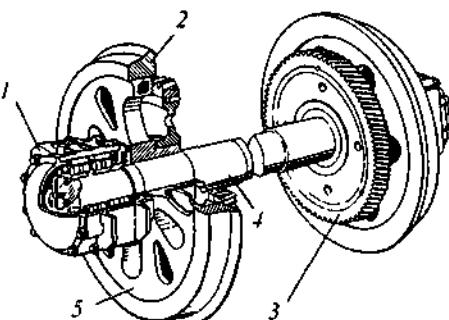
Колесная пара: 1 — корпус буксы; 2 — бандаж; 3 — зубчатое колесо; 4 — ось; 5 — колесный центр
